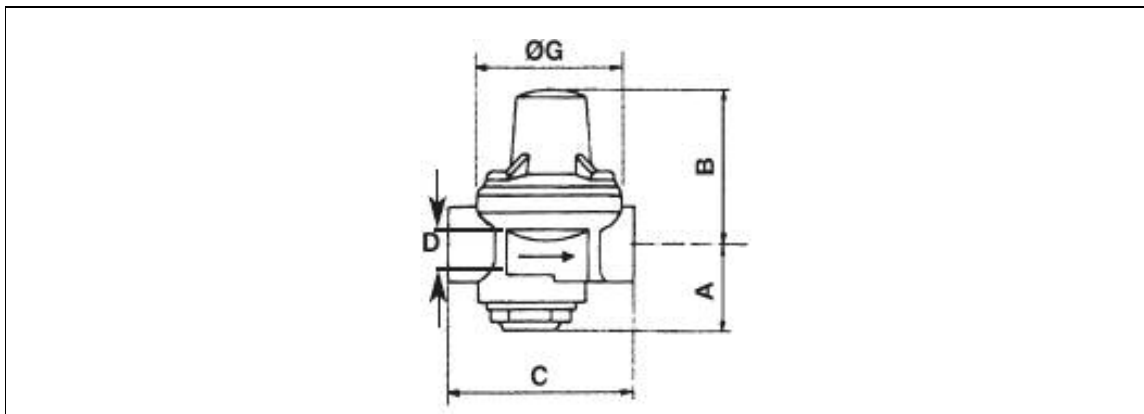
Габаритные и присоединительные размеры клапана редукционного типа 7BIS.
